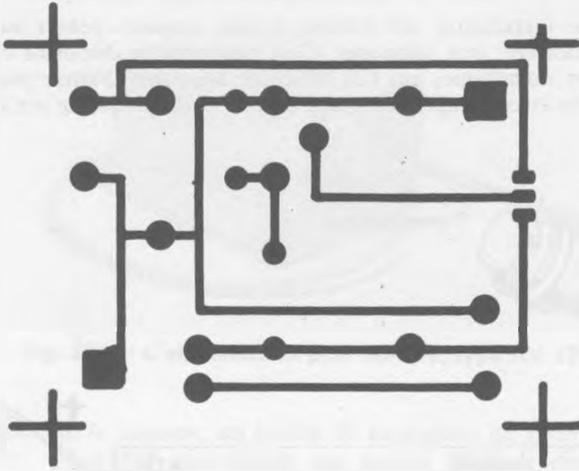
Le circuit imprimé, vu côté soudage
